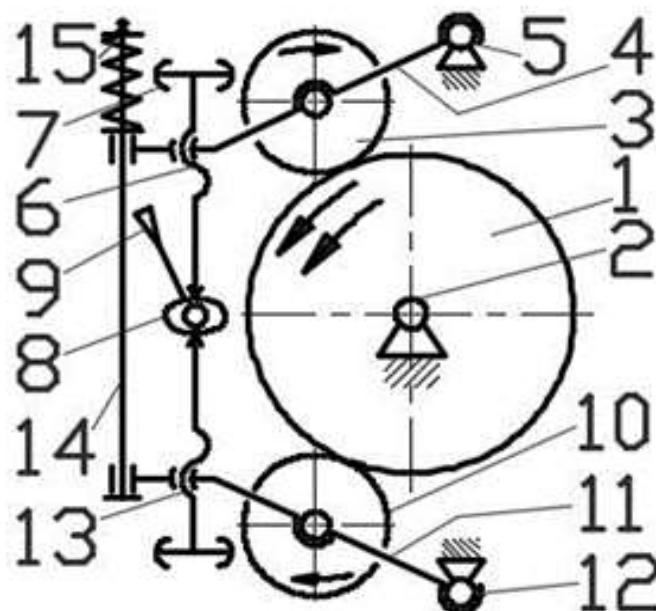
Схема установчого механізму вальцьового верстата.
